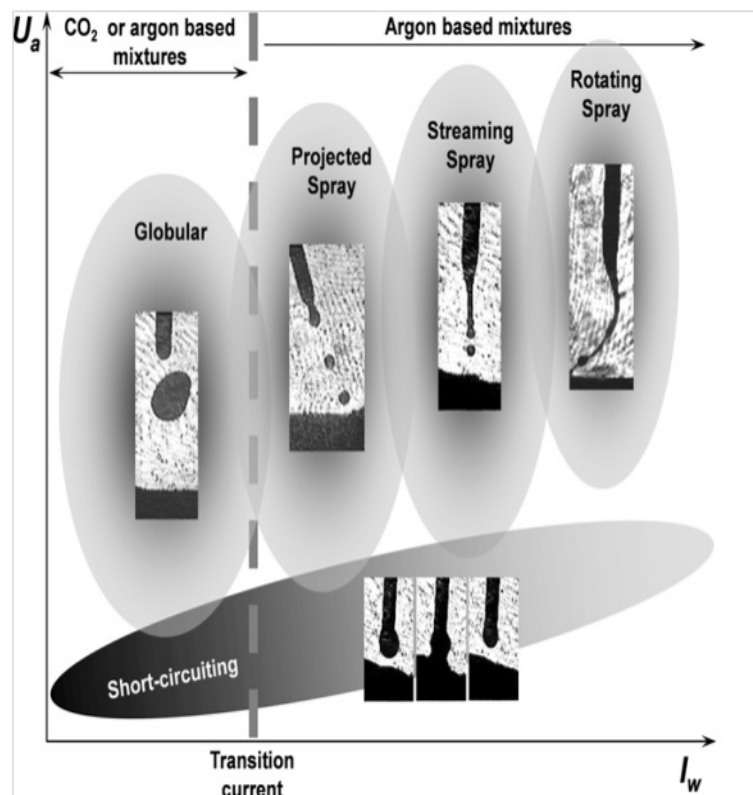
Carte des modes de transfert de métal en soudage MIG [8].
